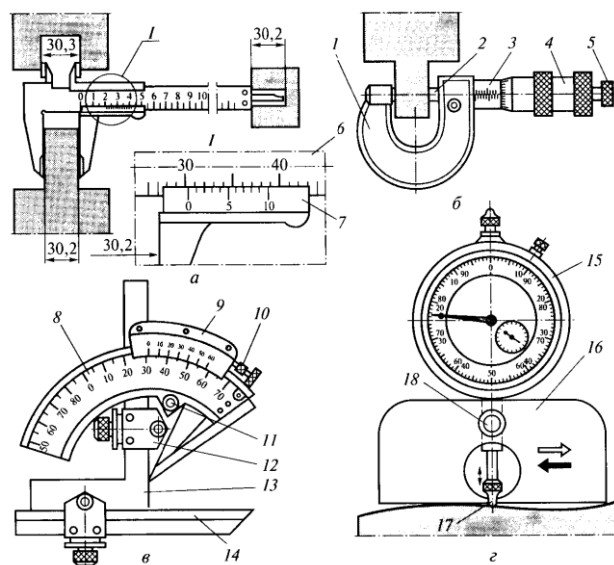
Вимірювальні інструменти: а – штангенциркуль; б – мікрометр; в – кутомір; г – індикаторний глибиномір; 1 – скоба; 2 – мікрометричний гвинт; 3 – стебло; 4 – барабан; 5 – тріскачка; 6 – основна шкала; 7, 9 – ноніуси; 8 – основа; 10 – гвинт настроювання; 11 – стопор; 12 – державка; 13 – косинець; 14 – знімна лінійка; 15 – індикатор; 16 – основа; 17 – наконечник; 18 – гвинт
